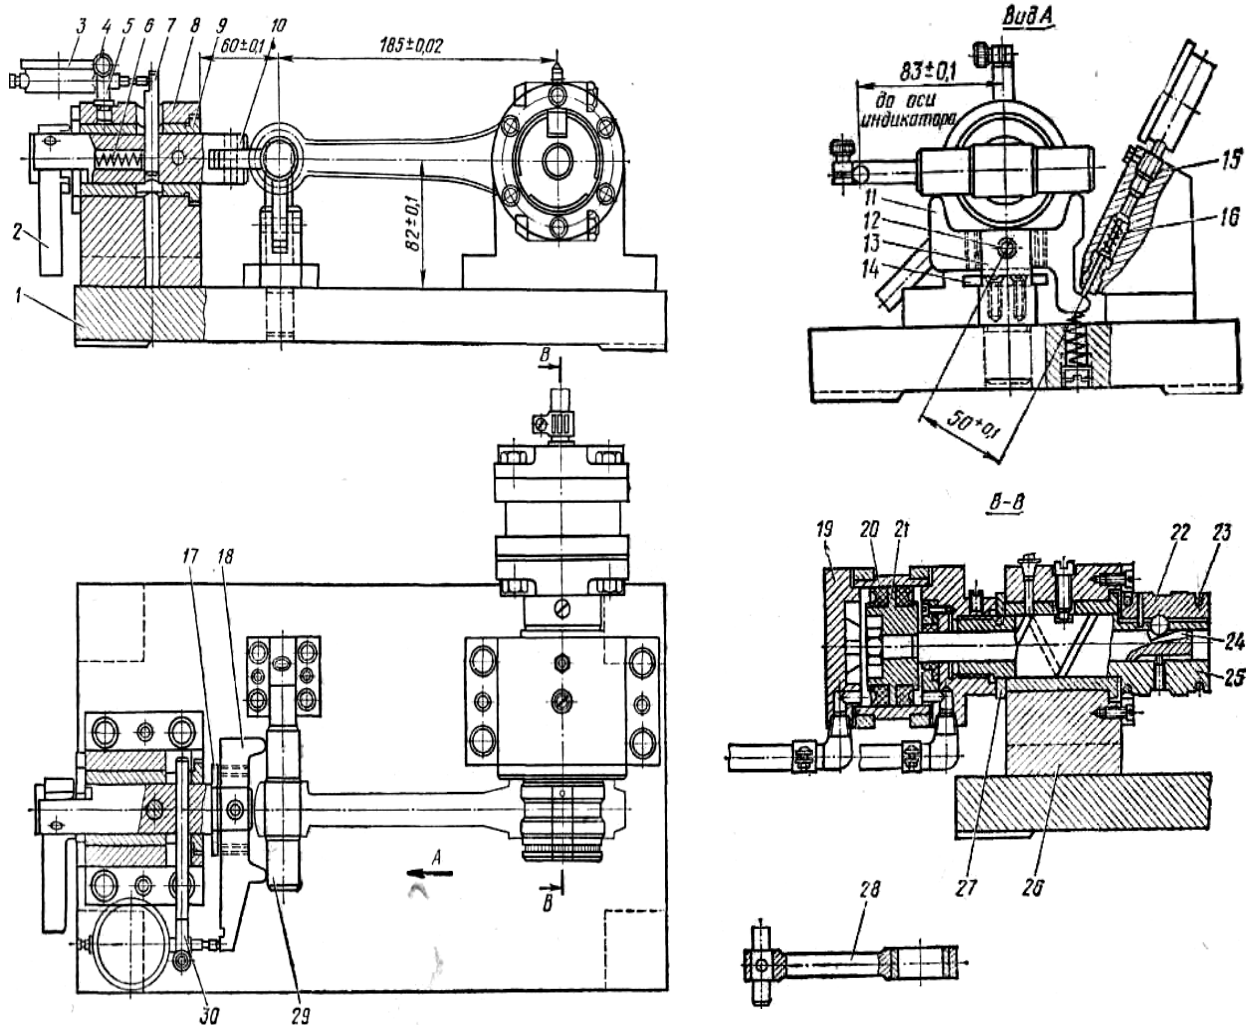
Пристосування для перевірки геометричних параметрів шатуна: 1 — плита; 2 — відведення; 3 — індикатор; 4 — гвинт; 5, 15, 26 — стійки; 6 — пружина; 7 - 13 — 17 — планка; 19—кришка; 20 — циліндр; 21 — поршень; 22 — сухар; 23 - кулька; 24 — шток; 25-палець; 8-корпус; 9-втулка; 10 - плунжер; 11 і 18- важелі; 12 і 16 - штіфти; 14 і 25- шпіндель; 27 - шайба; 28 - еталон; 29 - оправка; 30 - кронштейн
